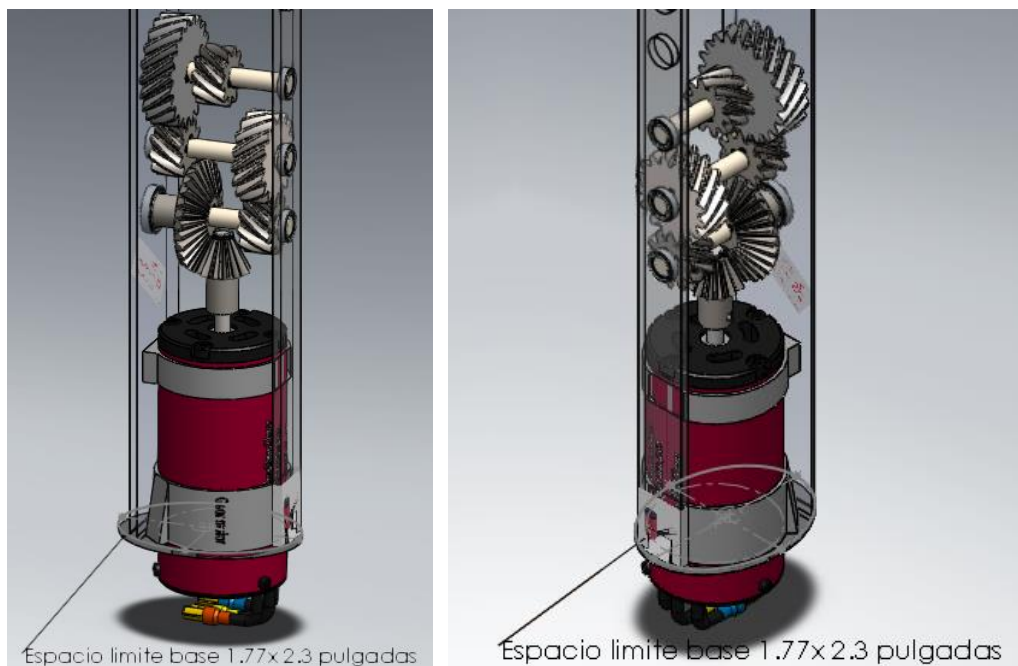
Vistas dimétricas de la etapa 1 del ensamblaje. Fuente propia.
